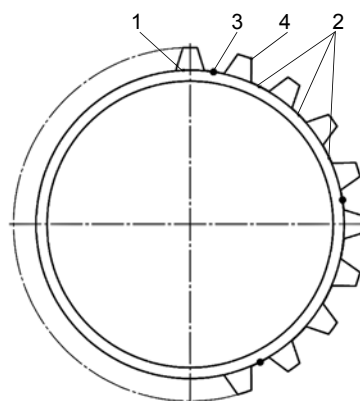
Конструктивная схема венцовой шестерни с зубчатым венцом из гнутого профиля: 1 — сварной корпус венцовой шестерни; 2 — места тангенциальных сварных швов; 3 — продольный сварной шов между смежными сегментами зубчатого венца; 4 — гнутый профиль зубчатого венца
